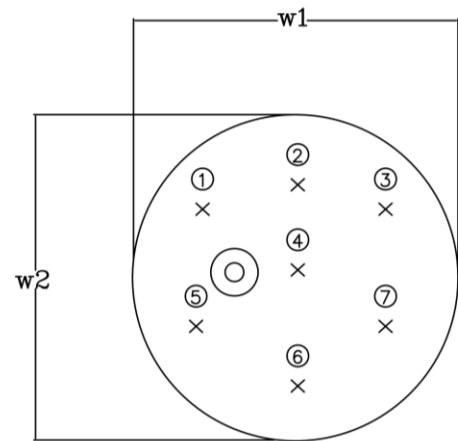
The position of spot checking for 19 kV single-phase transformers
